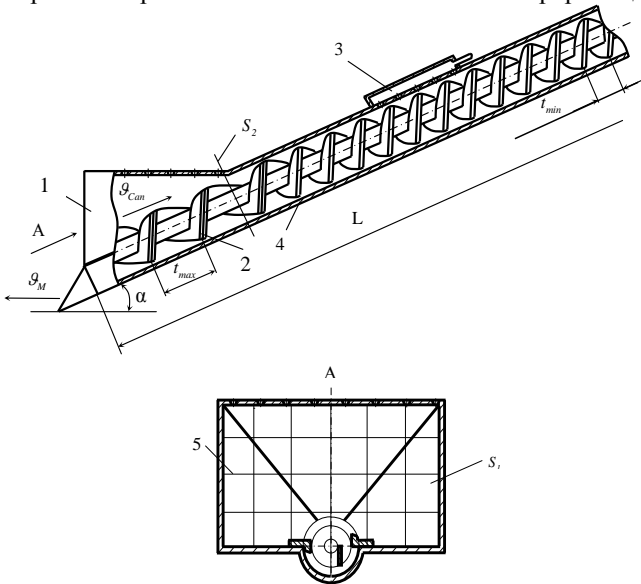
Схема модуля для добування озерного сапропелю: 1 – забірна частина; 2 – робочий орган із змінним кроком; 3 – камера збирання вільної води; 4 – корпус пристрою; 5 – захисна решітка
